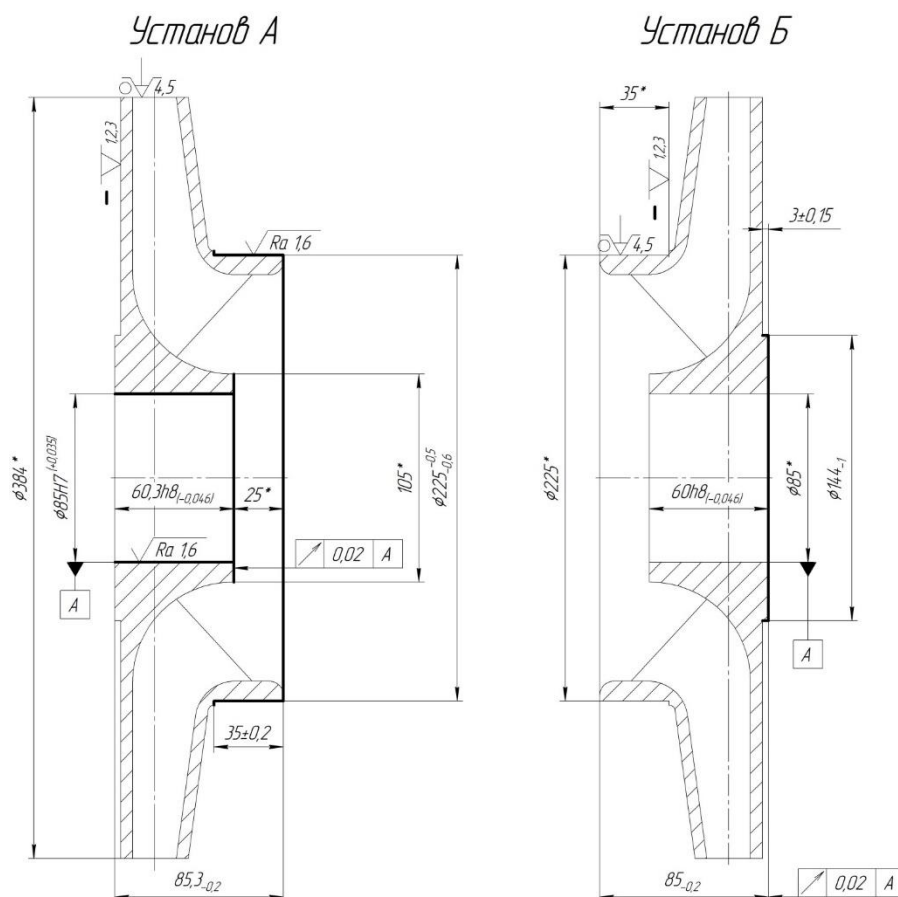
Схема установки заготовки на токарній операції (варіант 1)
